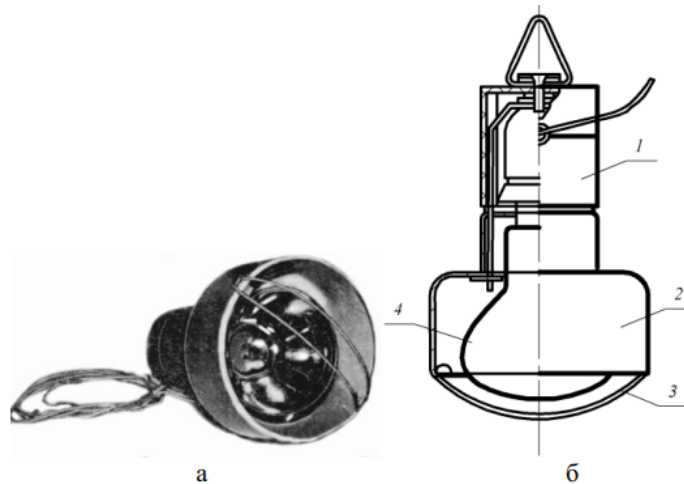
Опромінювач ветеринарний типу ОВИ-1: а) загальний вигляд; б) розріз: 1 – корпус; 2 – пластмасовий ковпак; 3 – захисна сітка; 4 – ІЧ-лампа
